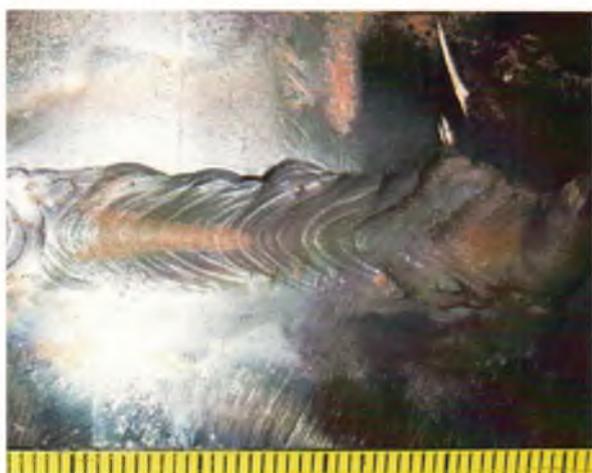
Стыковое сварное соединение трубопровода. Ручная дуговая сварка. Поверхность шва равномерная. Ширина шва порядка 8–10 мм. В кратере на участке гашения дуги наблюдается шлаковое включение 1
